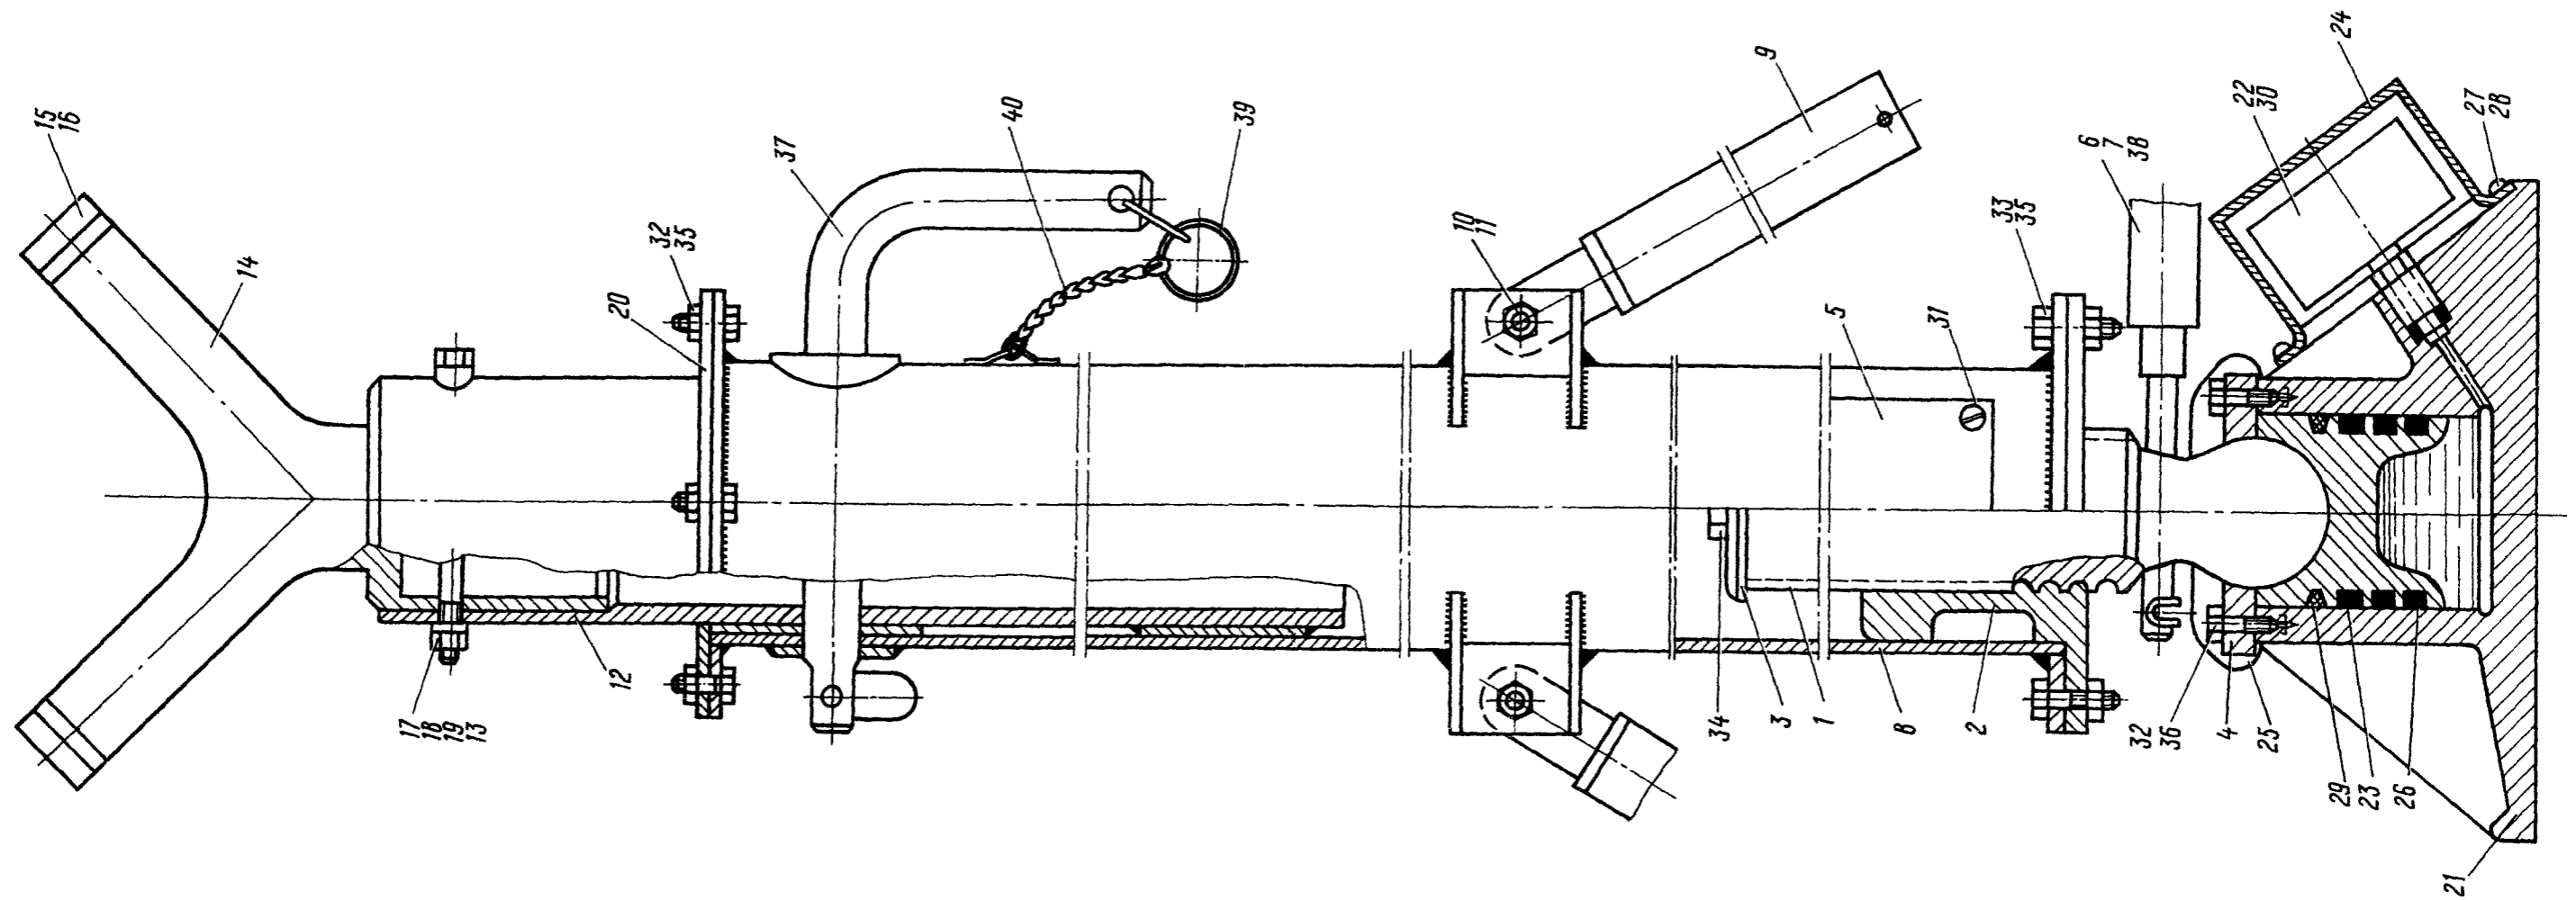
ПОДСТАВКА ПОД ДВИГАТЕЛЬ АИ-24
